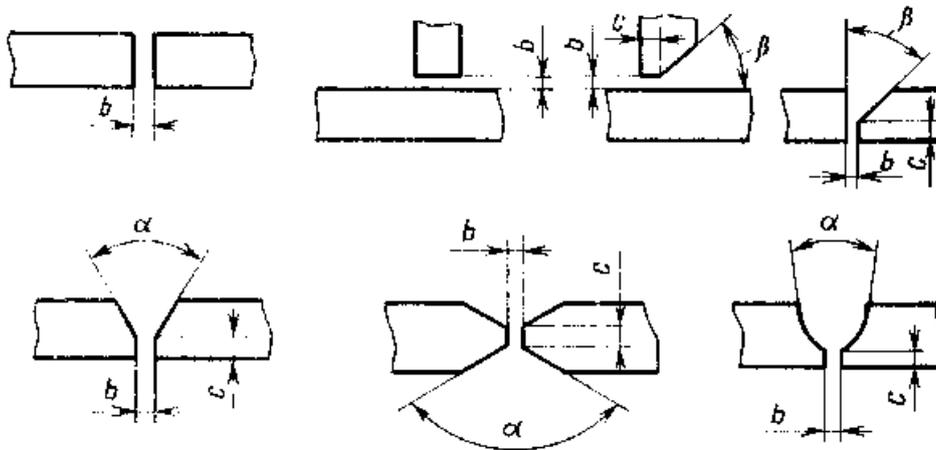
Конструктивные элементы деталей, подготовленных к сварке
